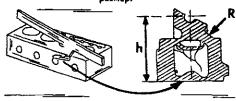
Расположение маркировки "R" на блоке цилиндров и на прокладке головки цилиндров. Высота головки "h" измеряется между стрелками.
